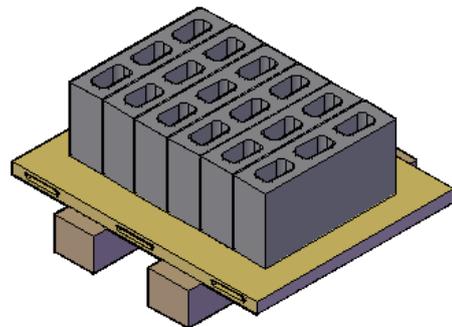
Usulan Rancangan *Pallet* Batako Tampak Depan
